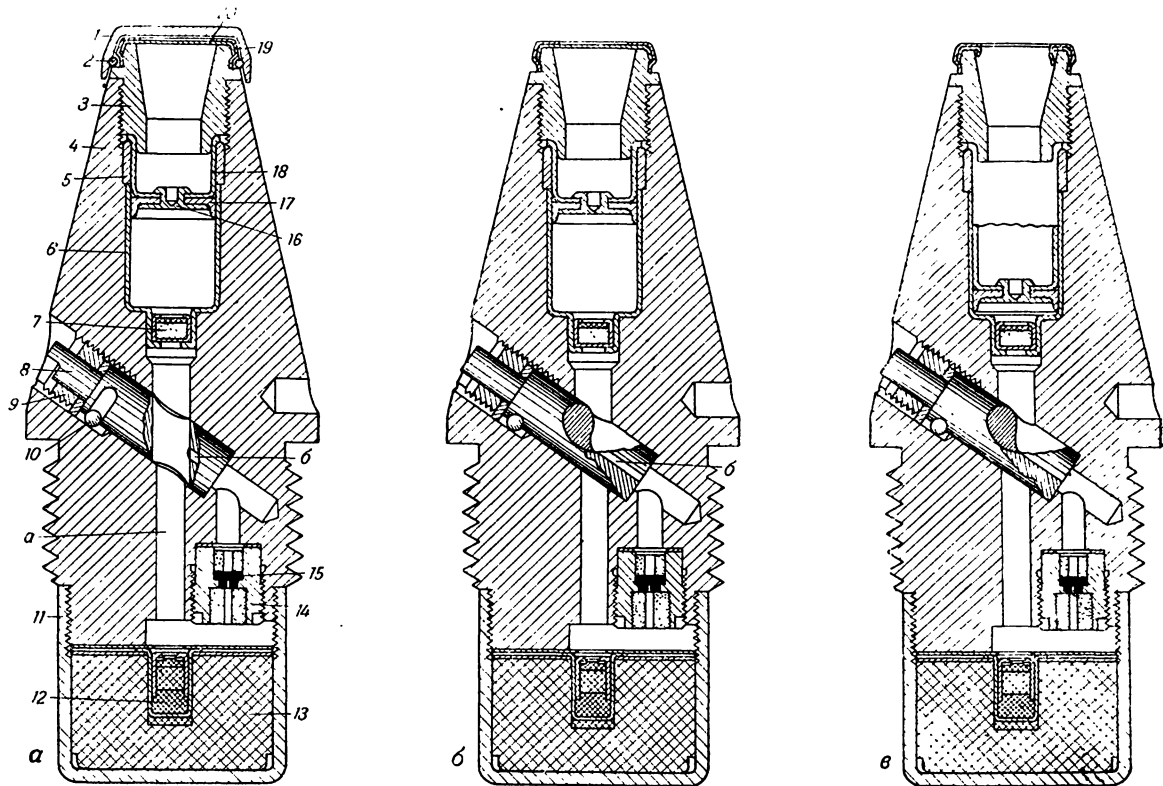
Устройство и положение деталей взрывателя ГВМЗ:
